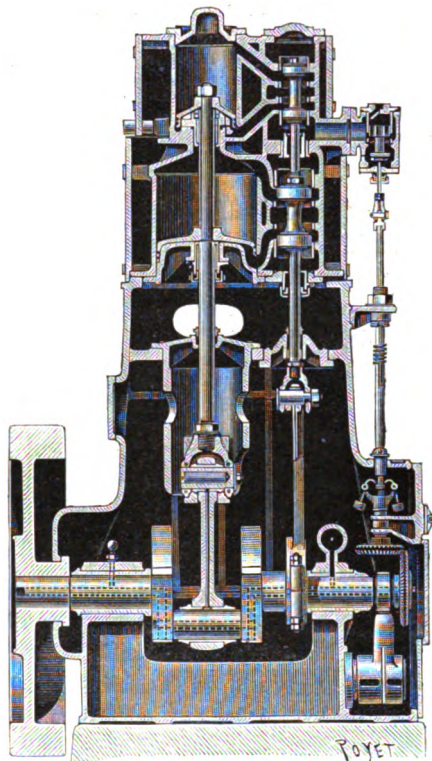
Coupe de la machine Boulte et Larbodière.
